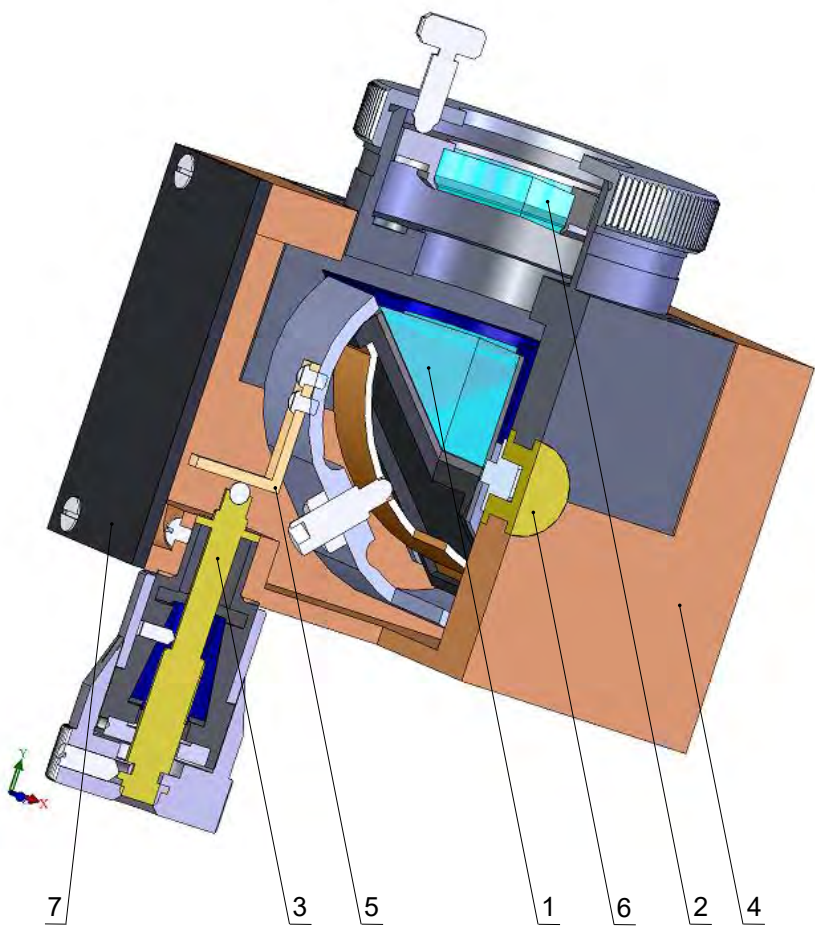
Конструкция механизма юстировки и крепления призмы АР-90°
